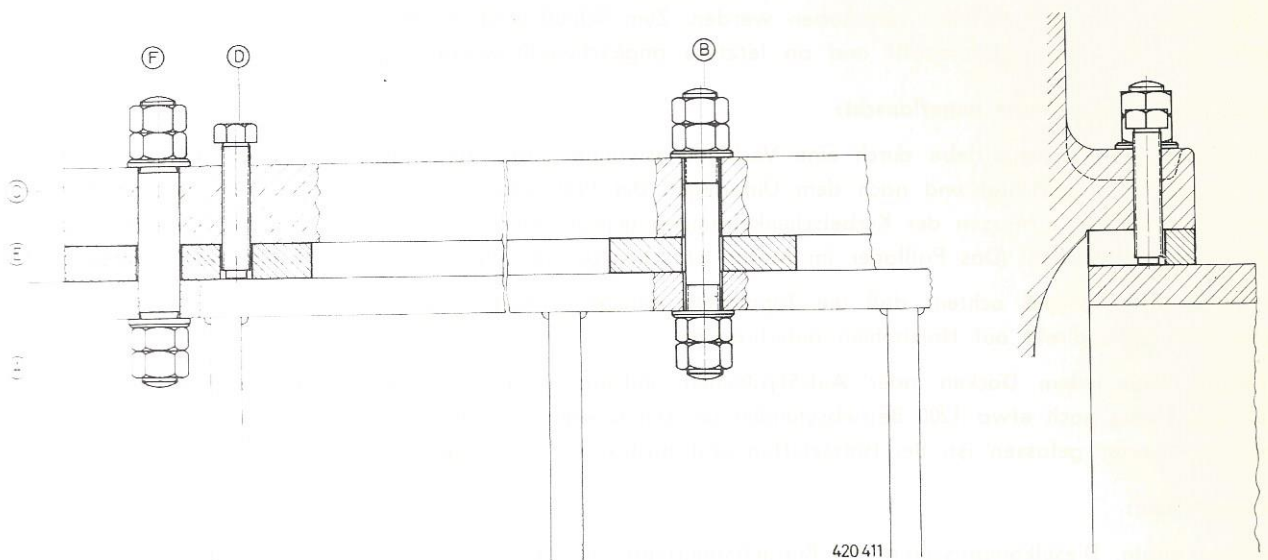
Ausrichten des Motors auf einem geschweißten Fundament
